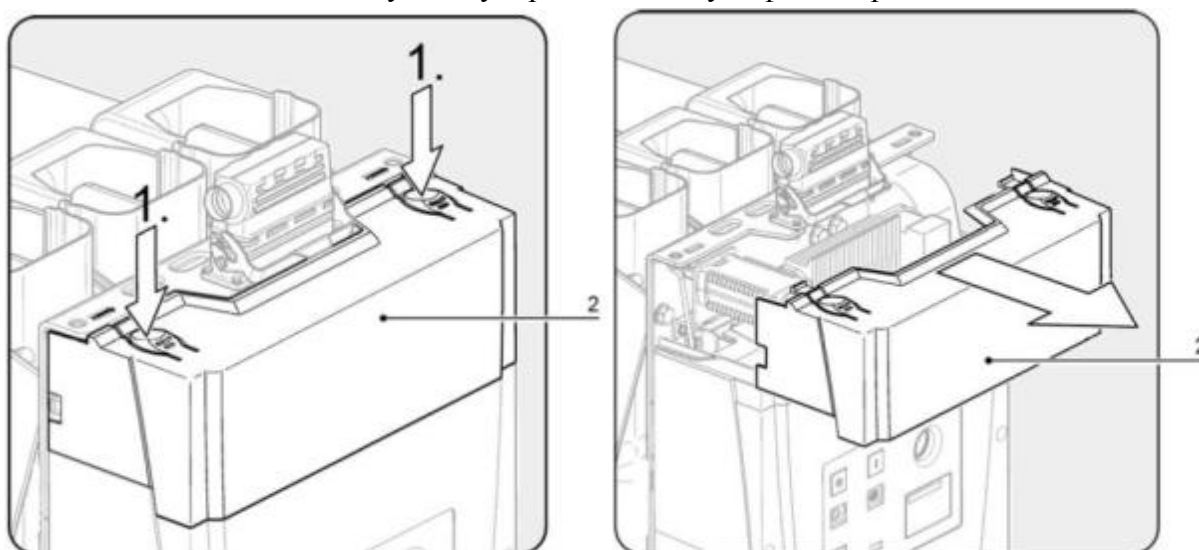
Демонтаж верхней крышки привода ВВ-БЭМН
